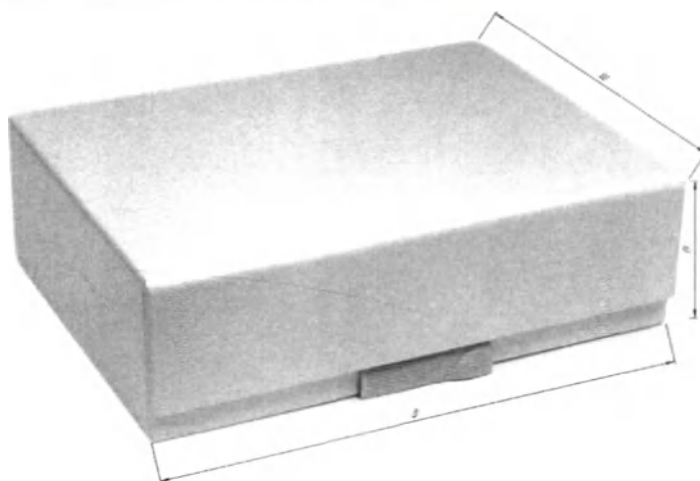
Внешний вид и размеры картонной упаковочной коробки без упаковочного рукава
